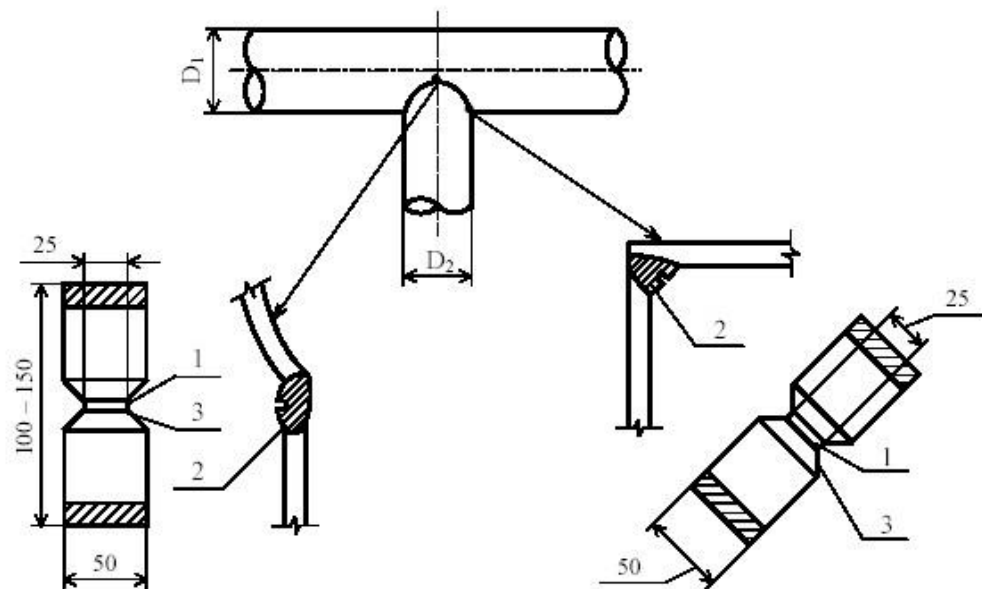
Схема испытаний на статический изгиб сварного соединения
